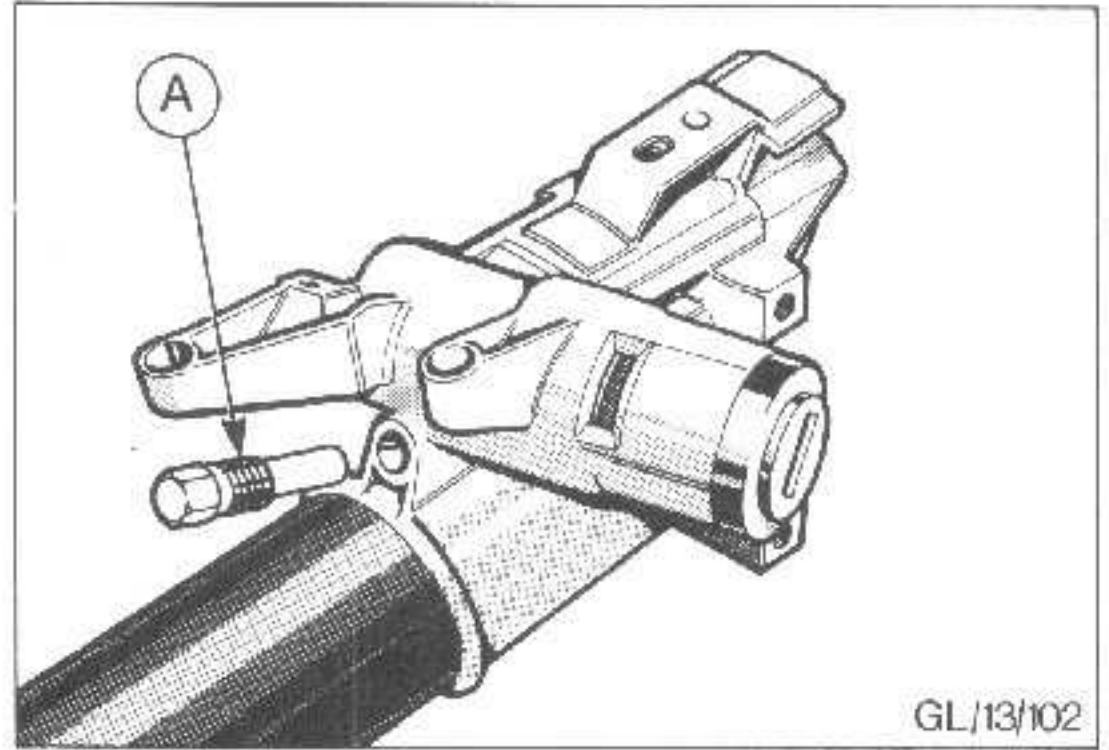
Abreißschraube - Lenkzündschloßbefestigung
